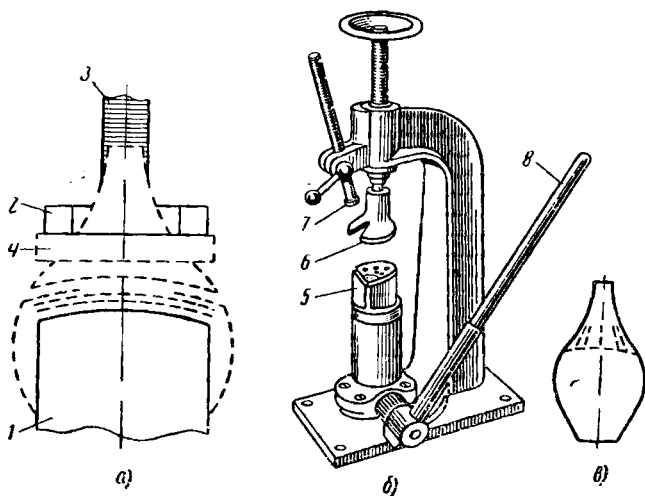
Приспособления для прикрепления каблучков изнутри обуви:
